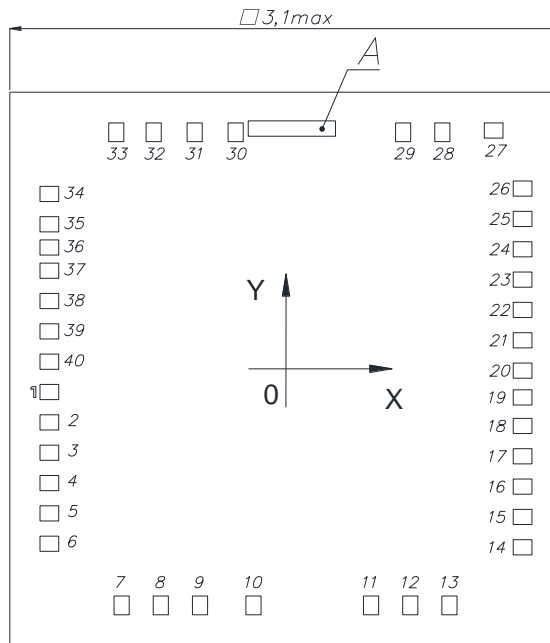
Габаритный чертеж микросхемы в корпусе N14.42-1B
